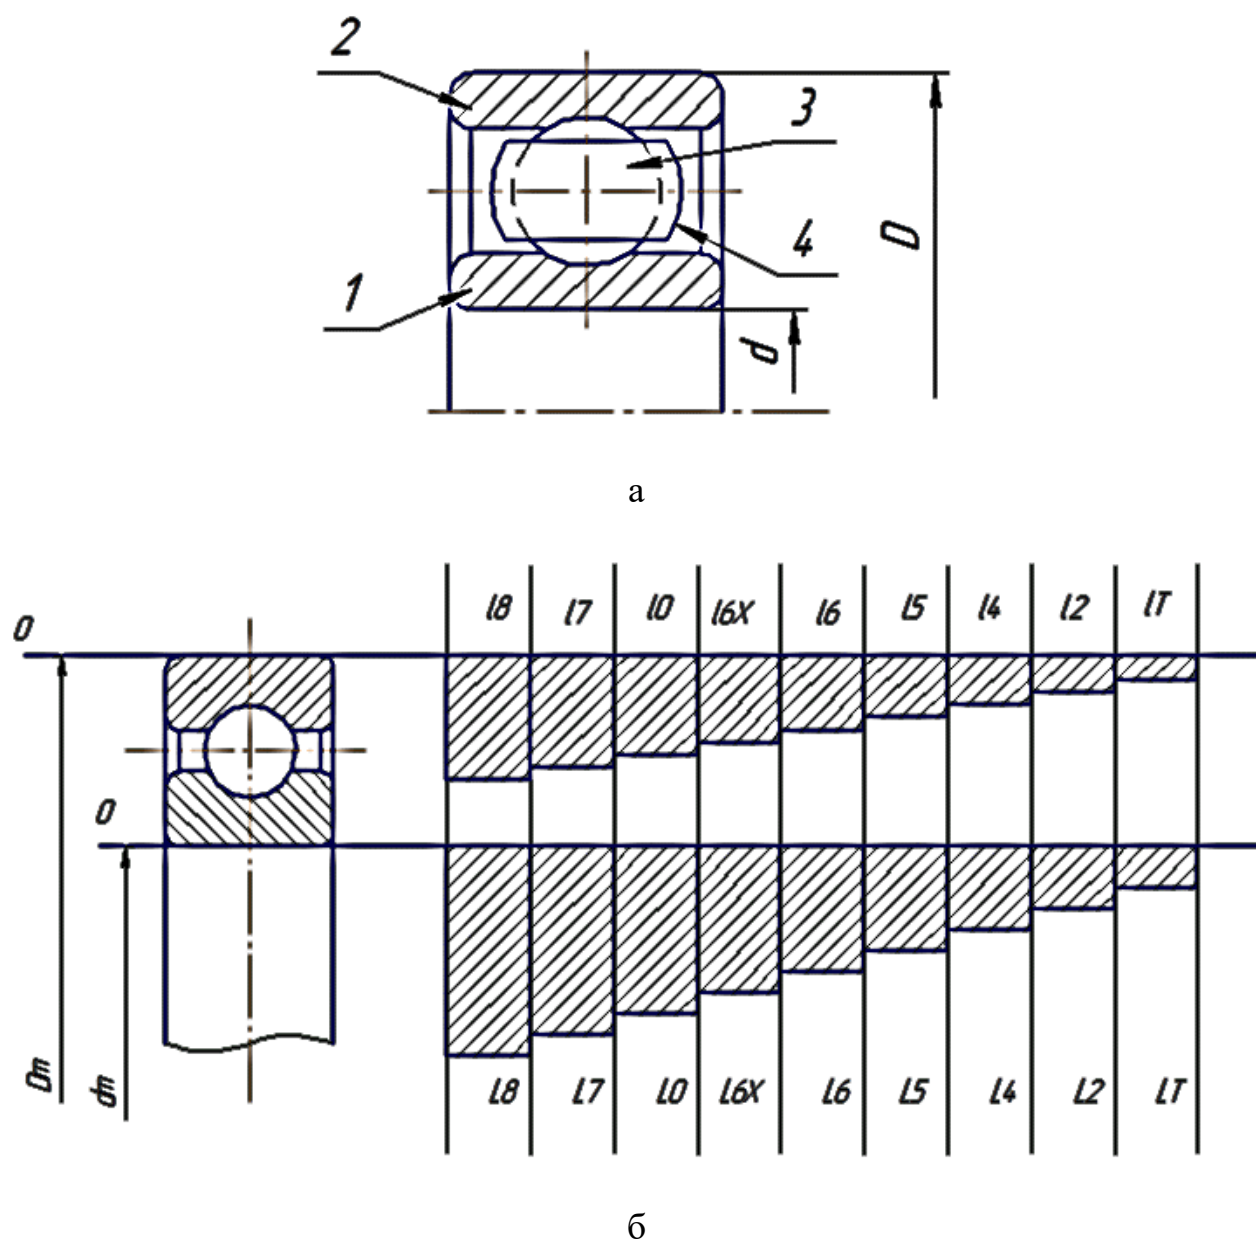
Шариковый однорядный подшипник качения: а - конструкция; б - схема расположения полей допусков по классам точности на средние наруж-
